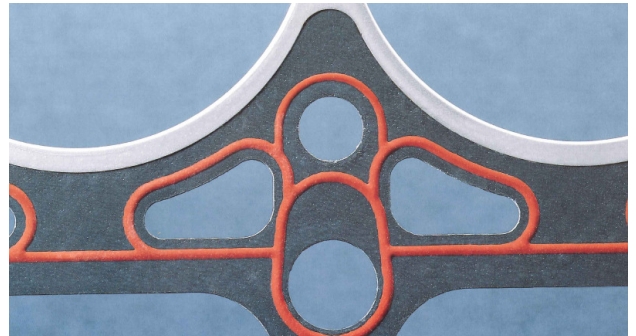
Druckölbereich mit roter Elastomerbeschichtung
